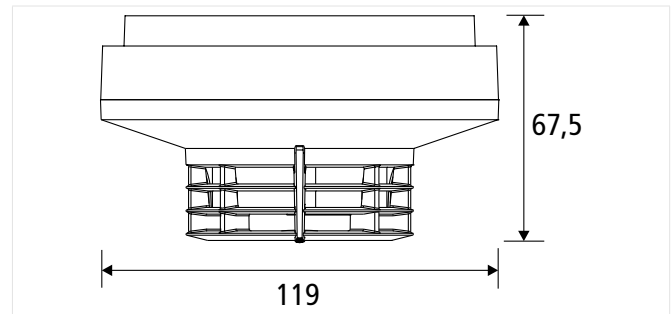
Seitenansicht mit Sockel USB 502-1/-6
